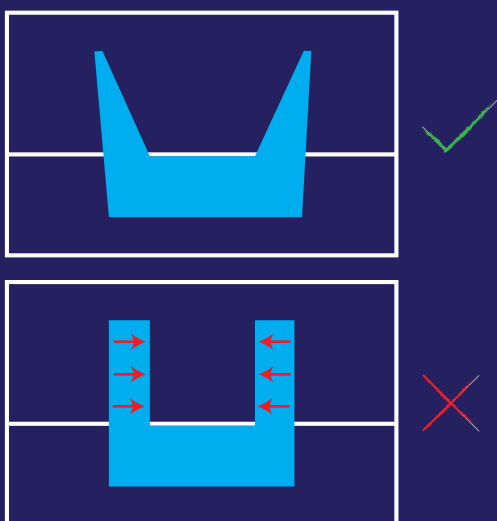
Molde simple con y sin consideraciones para el desmolde de las piezas.
